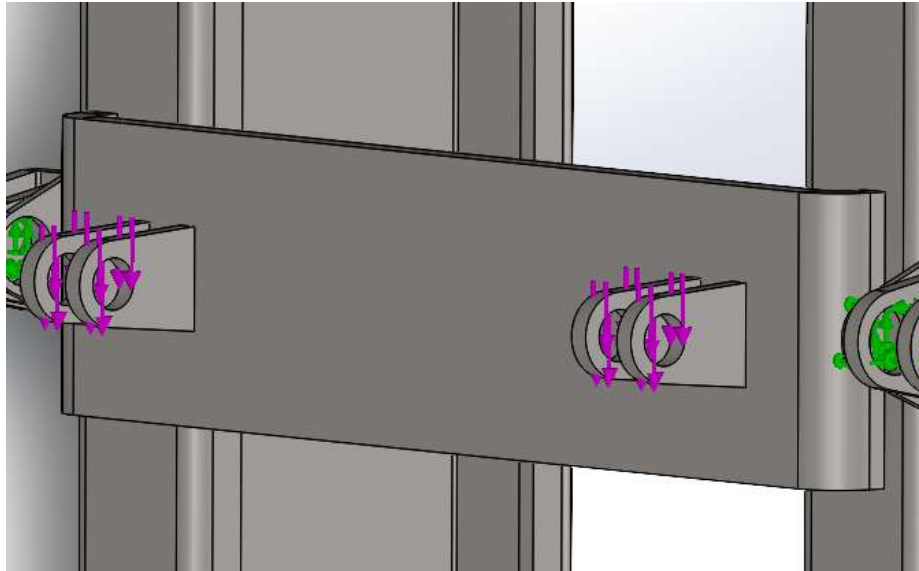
Aplicación de fuerzas para situación con carga vertical.
